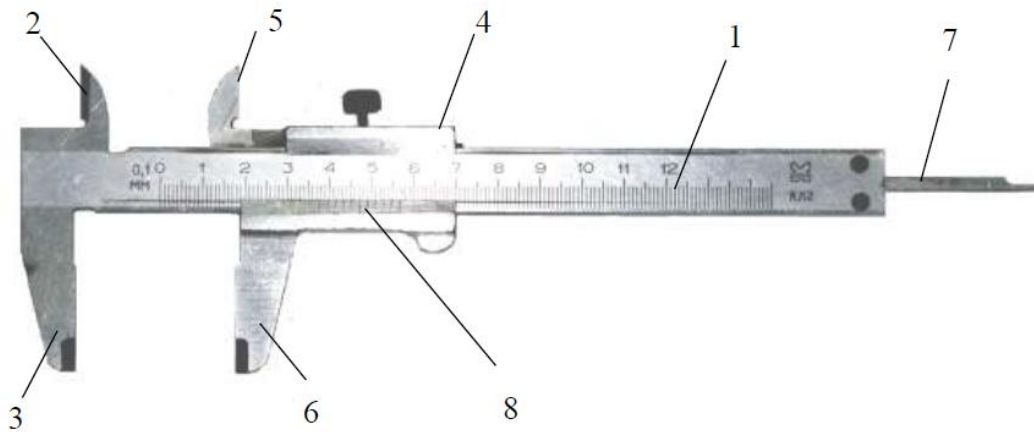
Штангенциркуль типу ШЦ-I
